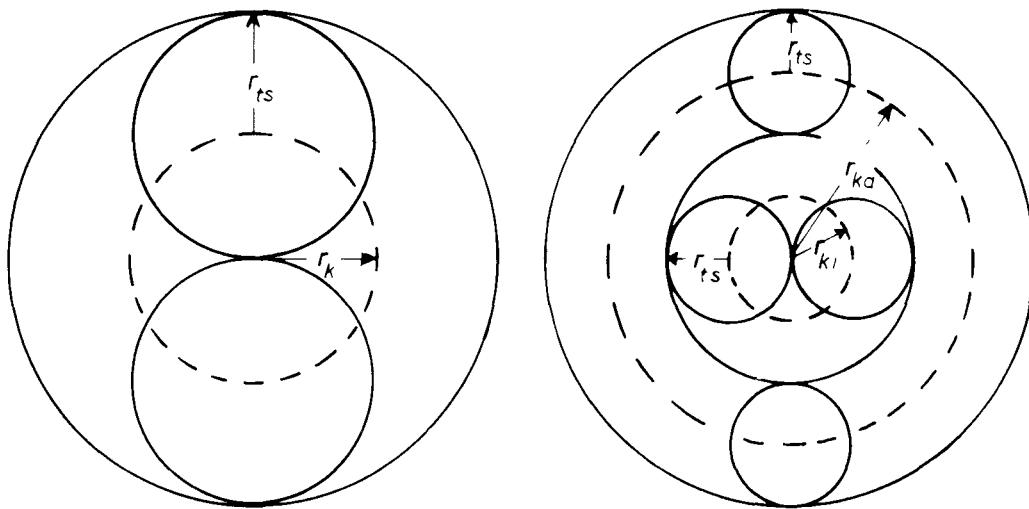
Tête de fraisage à une zone planétaire (à gauche) et à deux zones planétaires (à droite)
